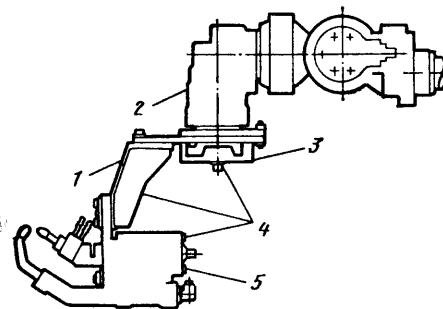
Предохранительная муфта: 1 — кронштейн; 2 — присоединительный фланец; 3 — муфта; 4 — рабочий орган; 5 — сварочная головка
